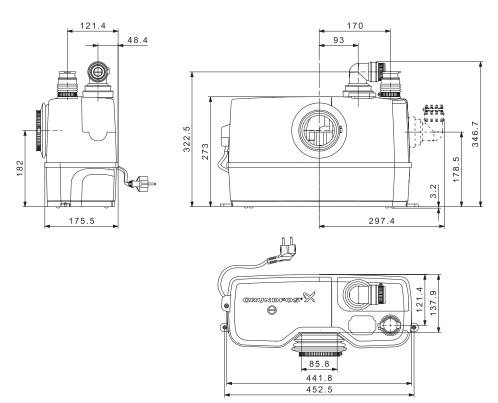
Габаритные размеры, SOLOLIFT2 WC-1
